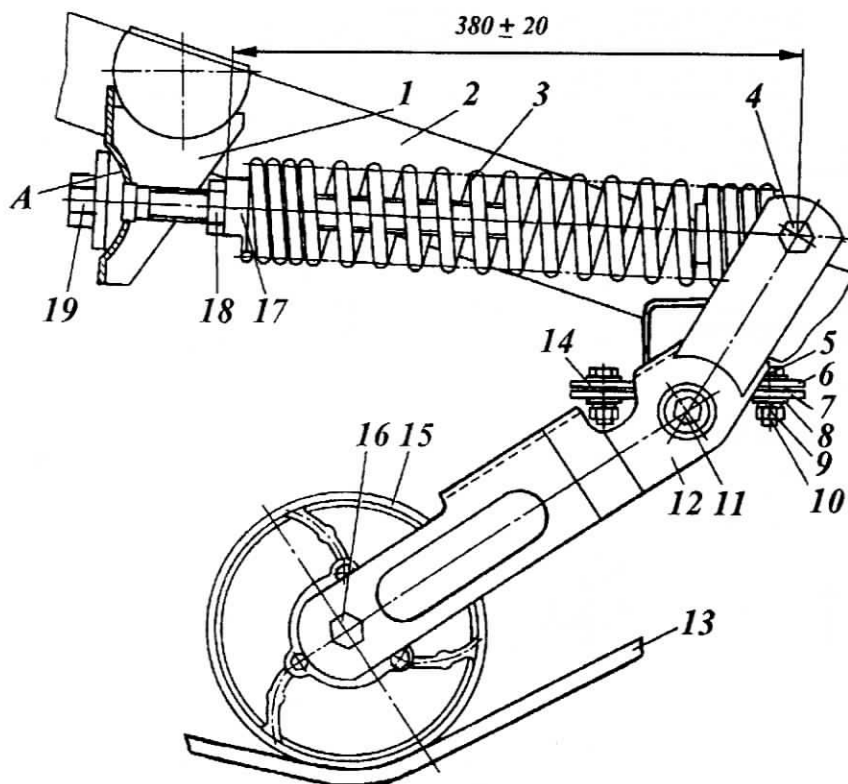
Механизм натяжения ремней привода измельчающего барабана.
